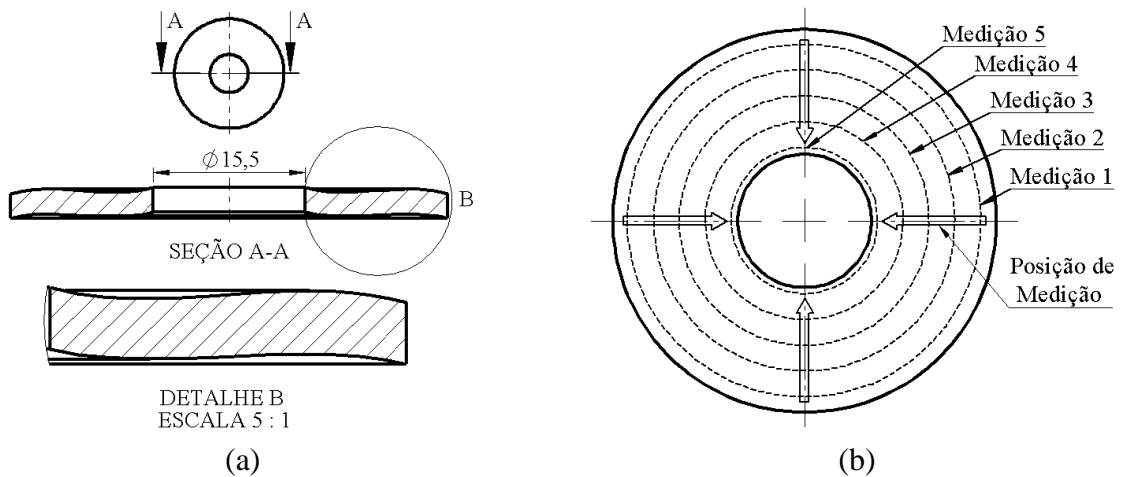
Medição do desvio dimensional: (a) deformação geométrica da peça; (b) posições de medição.
